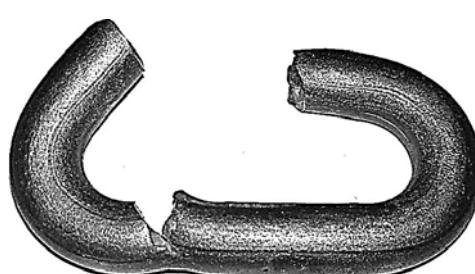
Вид разрушенного прутка в процессе пластического изгиба в заготовку круглой формы
